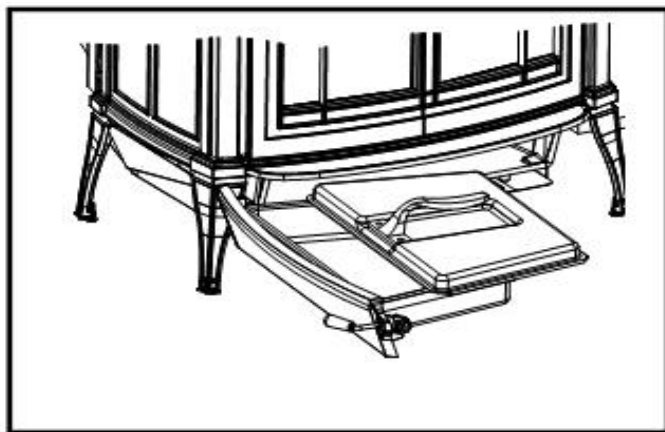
Поверните ручку дверцы пеплосборника по часовой стрелке для того, чтобы открыть его и против часовой стрелки – чтобы закрыть.
